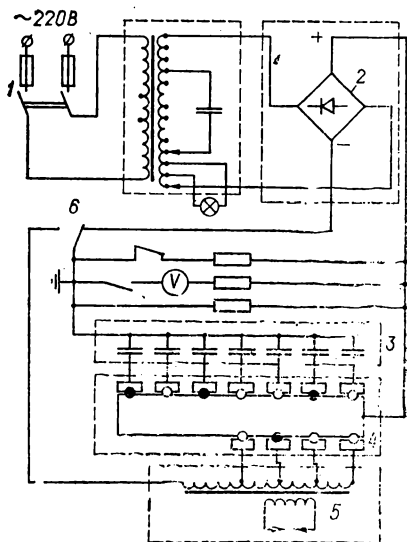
Схема сварочной конденсаторной машины:
